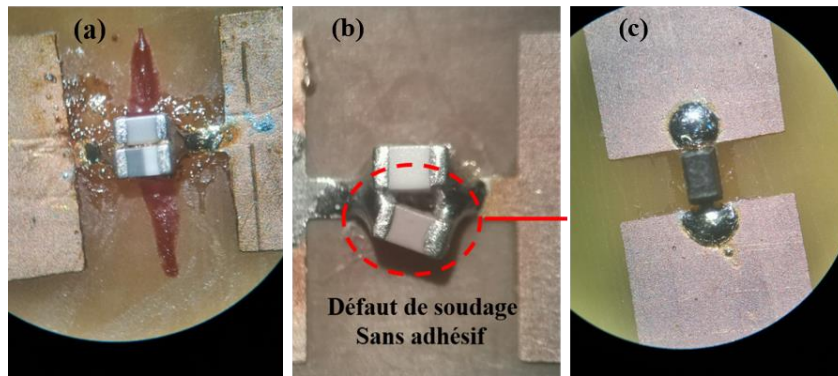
Photos sous microscope illustrant les soudures : (a) Circuit LC parallèle fixé avec l'adhésif Loctite 3609, (b) défaut de soudure d'un circuit LC parallèle sans utiliser l'adhésif, et (c) diode soudée sans adhésif.
